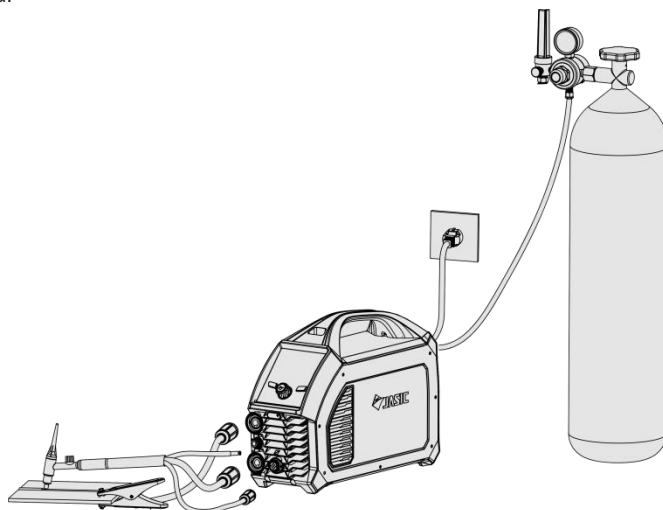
Подключение сварочной горелки, кабеля заземления и газового баллона
